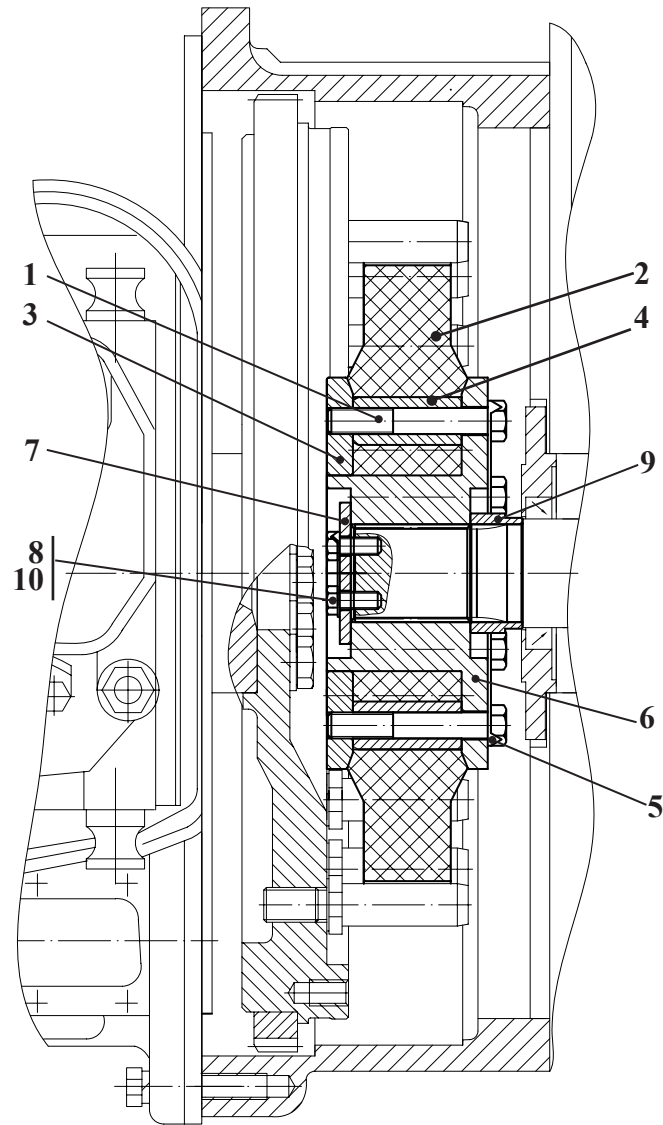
ТО-28А.02.00.900-Б	Установка демпфера
